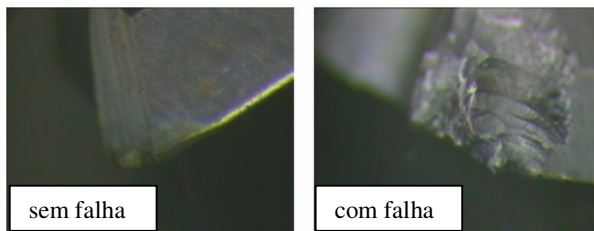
Fresa com gume postiço após usinagem do acrílico
